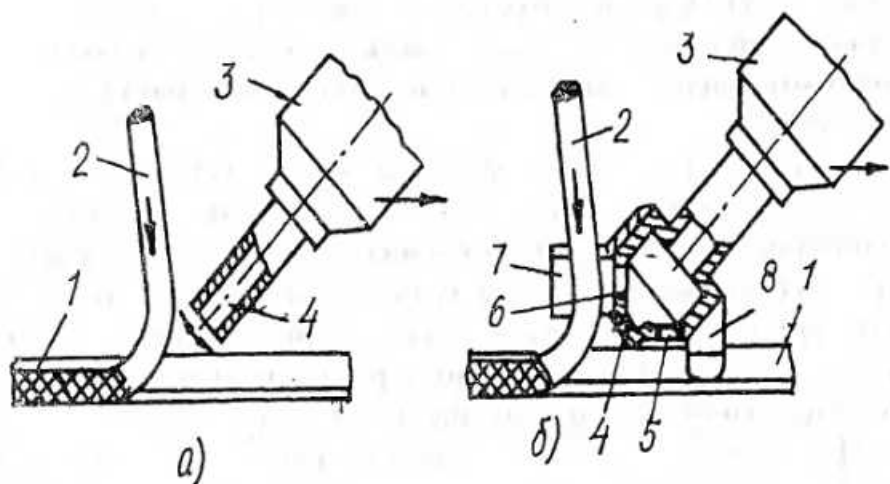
Схема ручного пруткового звичайного (а) і швидкісного (б) зварювання: 1 - зварювані деталі; 2 - пруток; 3 - зварювальний пальник; 4 - вихідний канал наконечника; 5, 6 - канали попереднього нагрівання; 7 - напрямна для прутка; 8 - напрямний клин
